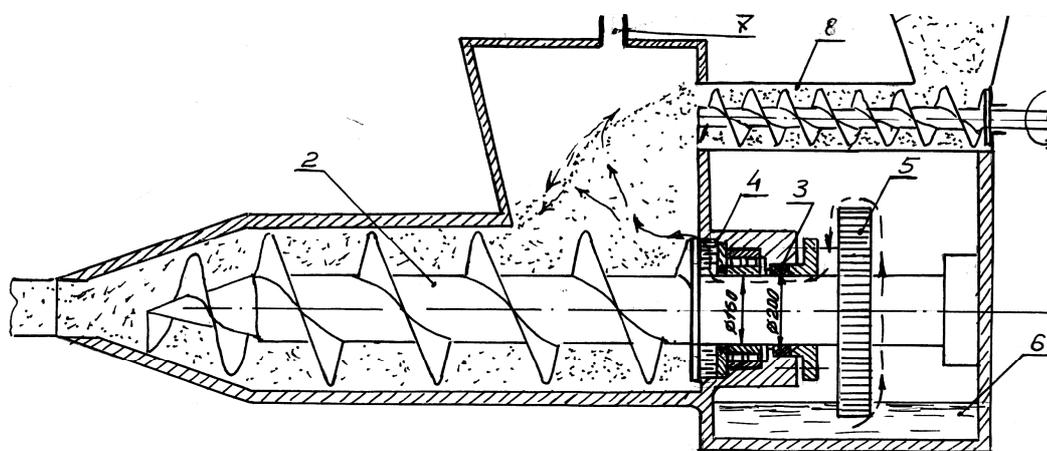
Конструктивное исполнение прессы для формирования глиняного бруса. Стрелками обозначен путь движения масла в формовочную смесь, подаваемую питателем 8: 1 – корпус прессы; 2 – шнек; 3 – сальниковая набивка; 4 – лабиринтное уплотнение; 5 – шестерня привода; 6 – поддон картера; 7 – вакуумкамера, 8 – питатель
